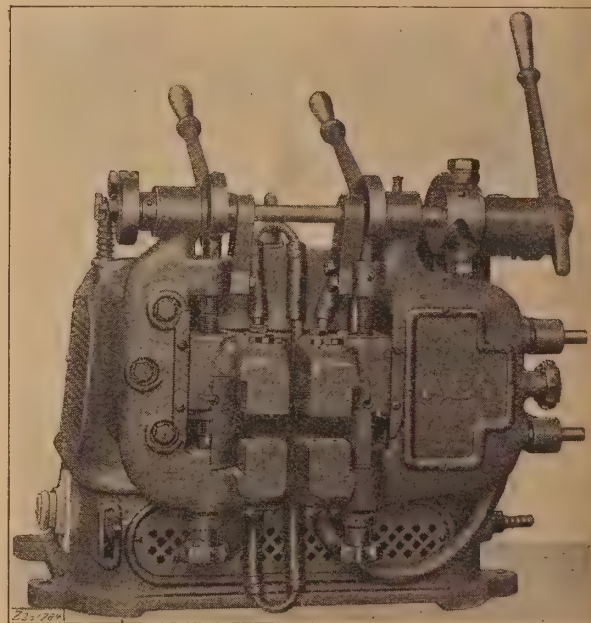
Neue Stumpfschweißmaschine der AEG.
